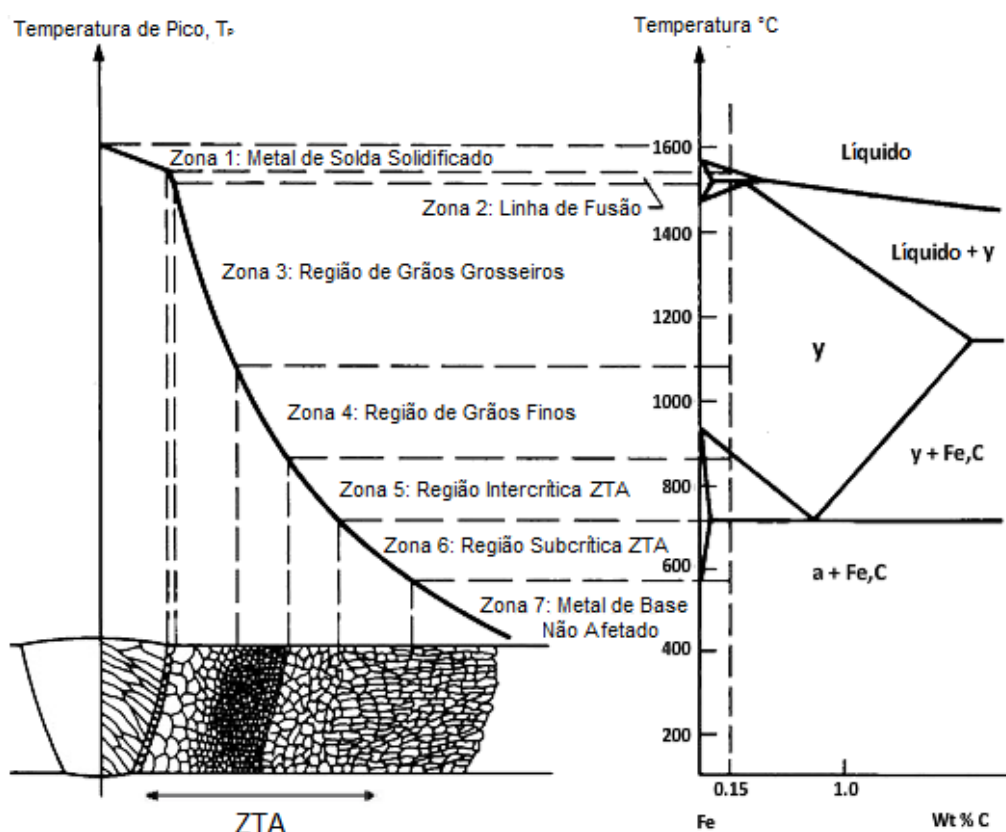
Microestrutura da junta soldada conforme temperatura de pico dos ciclos térmicos de soldagem em aço carbono com 0,15% C.
